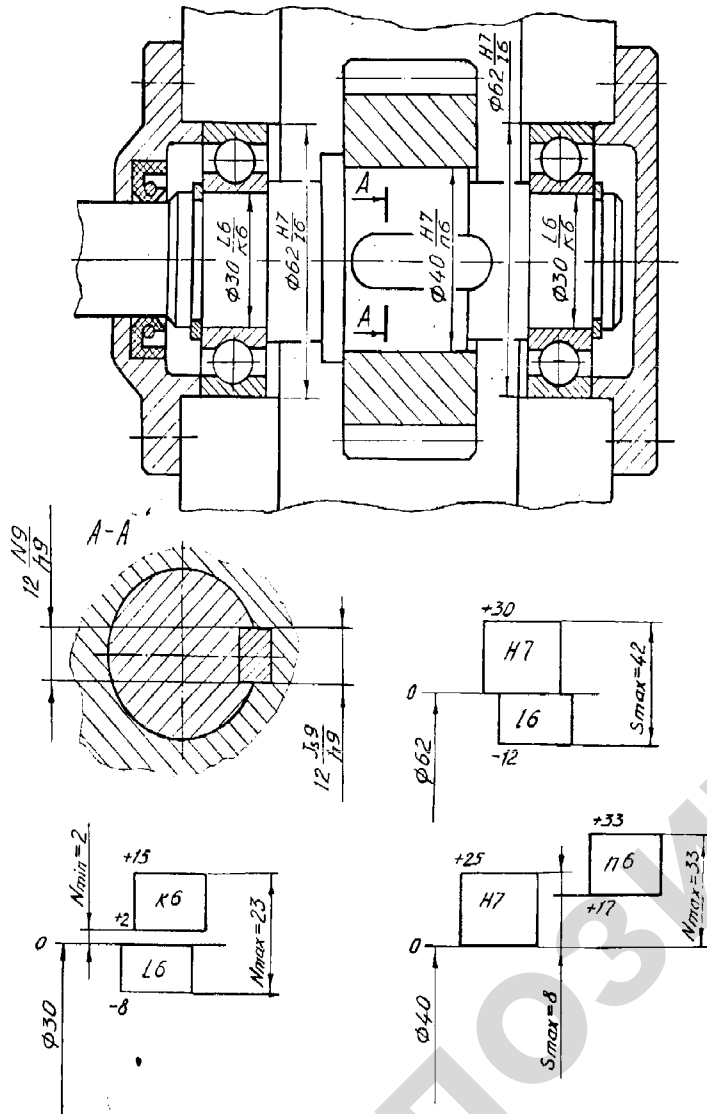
Первичный вал редуктора в сборе и схемы полей допусков соединений
